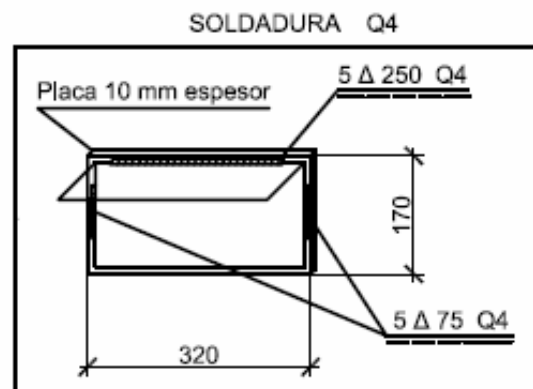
Detalle de un plano de soldadura de una palomilla
